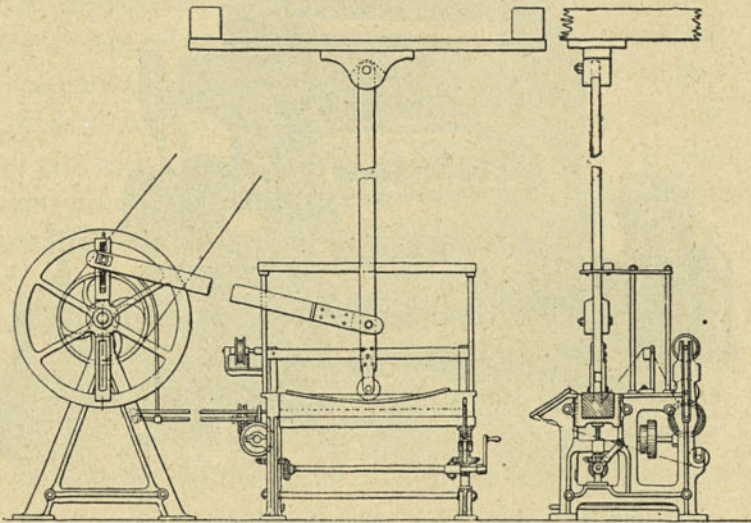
Machine à lustrer à la molette (vue de face et vue de côté).
